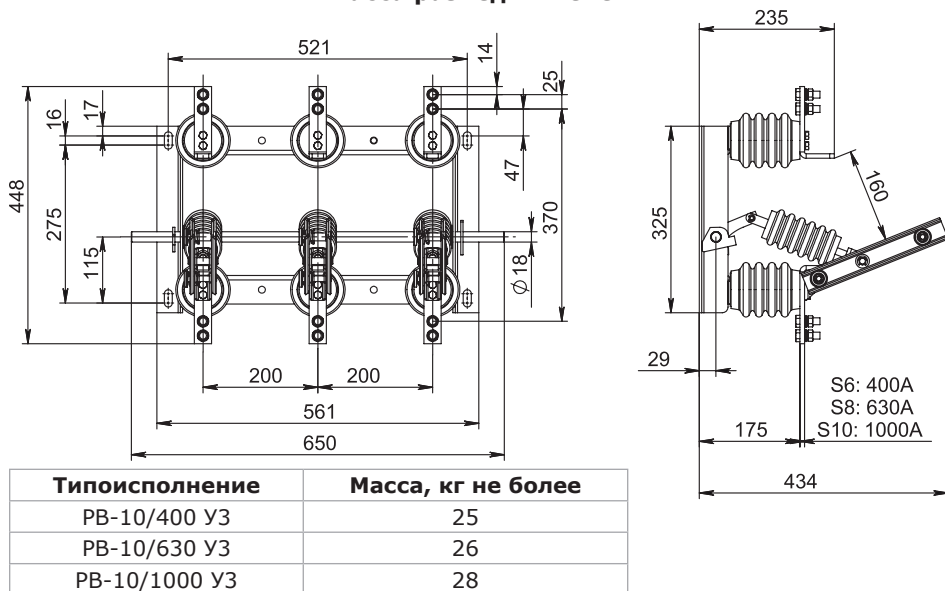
Разъединитель внутренней установки типа РВ
